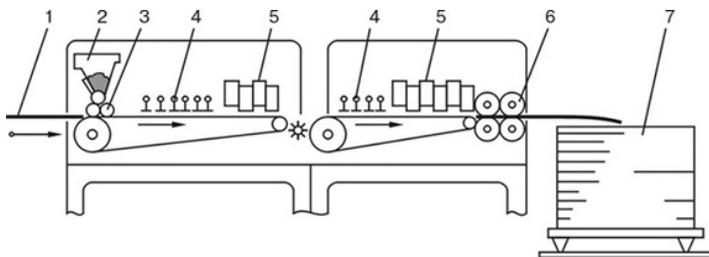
Схема бронзировавшего автомата: 1 — оттиск; 2 — бункер с металлической пудрой; 3 — накатные валики; 4 — растирочные щетки; 5 — очистные ремни; 6 — очистные валы; 7 — приемное устройство
